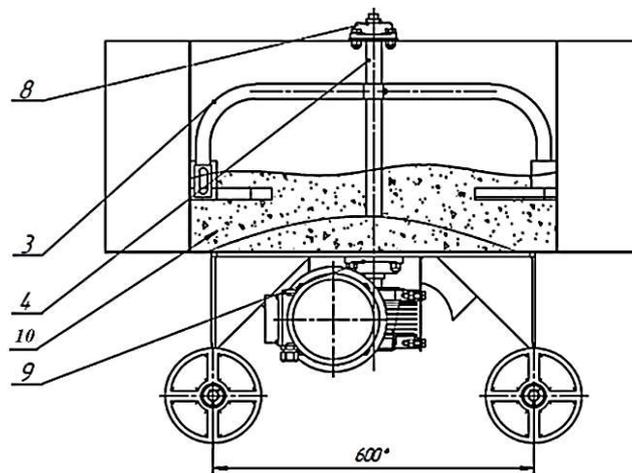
б. Вид справа установки: 3 – кронштейн (коромысло); 4 – приводной вал;
